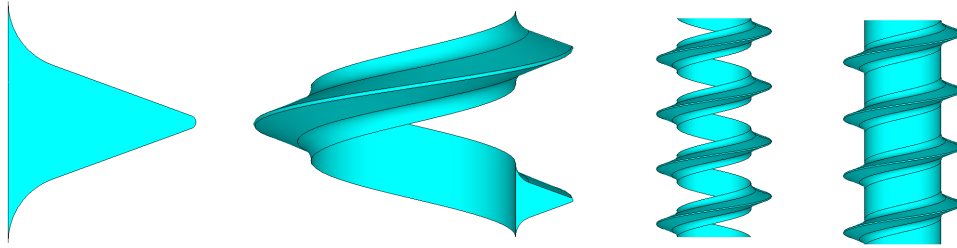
Erzeugen einer Schraubengeometrie mit Verrundungen
